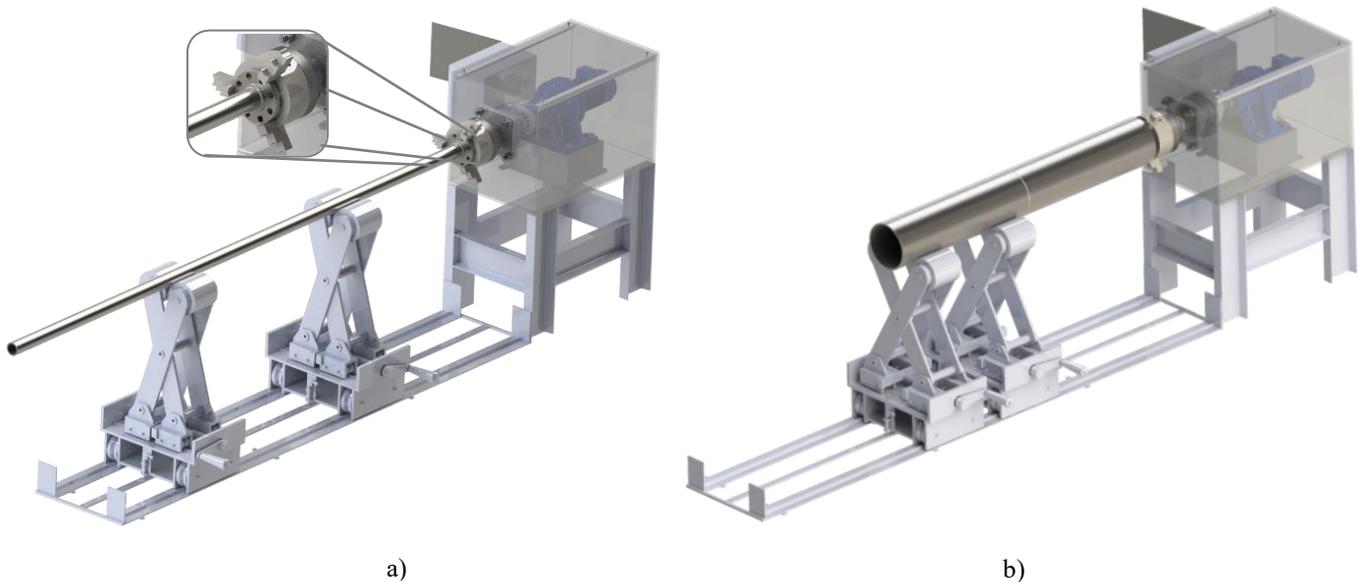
Configuración del sistema de soldadura para diferentes casos: a) Tubo de 64.90 mm de diámetro y 3 m de longitud soldada a una brida, b) Par de tubos de 203.2 mm de diámetro y 0.75 m de longitud soldados entre sí.
